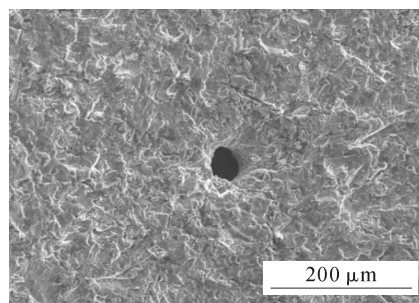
钛合金熔模精密铸件表面焊接引入性气孔
